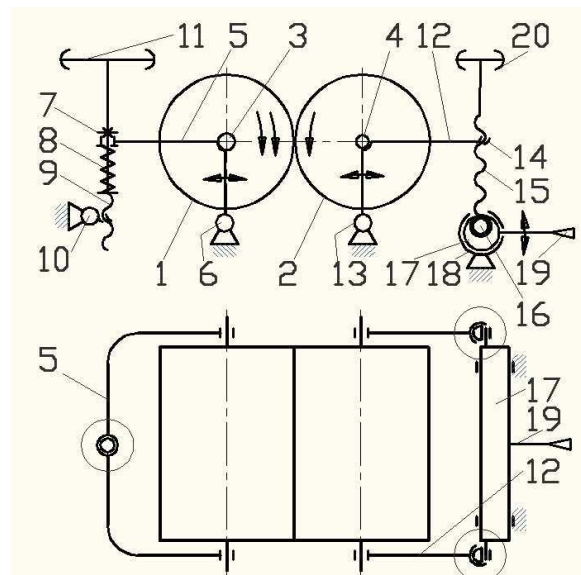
Конструкция установочного механизма с регулировкой двух вальцов
